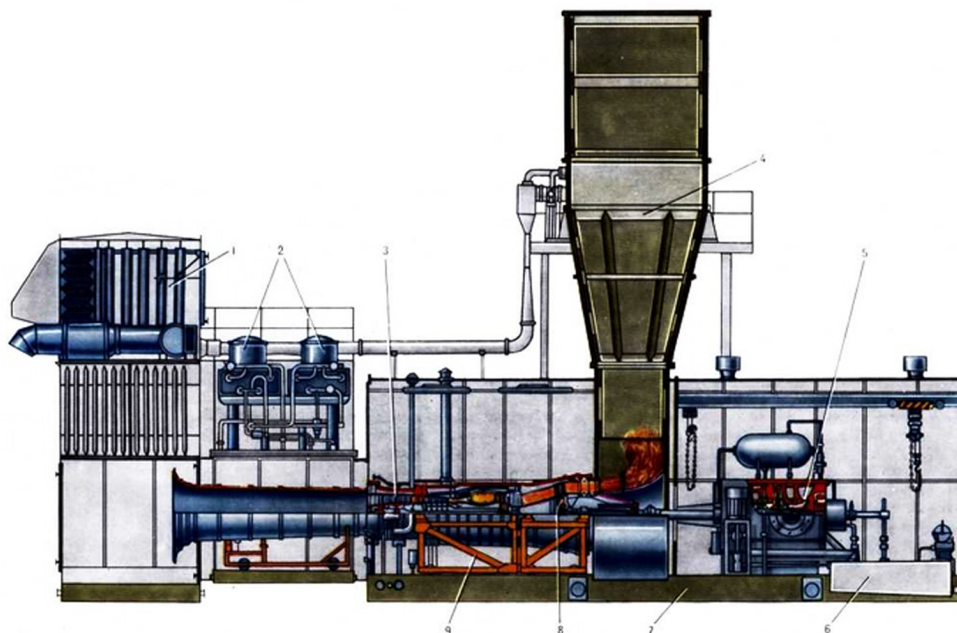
Газоперекачивающий блочно-контейнерный агрегат ГПА-Ц-16 с авиаприводом: 1 — входное воздухоочистительное устройство; 2 — масляные радиаторы; 3 — авиационный привод НК-16 СТ; 4 — выхлопное устройство с шумо глушителем; 5 — нагнетатель природного газа; 6 — маслобак агрегата; 7 — фундаментная металлическая рама агрегата; 8 — силовая турбина агрегата; 9 — подмоторная рама авиапривода
